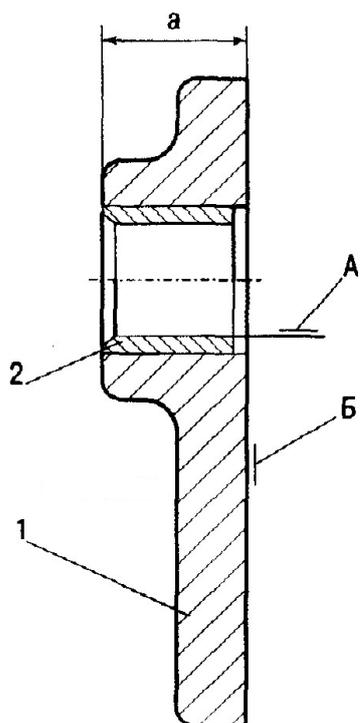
Крышка масляного насоса в сборе со втулкой: 1 - крышка; 2 - втулка; а - размер; А и Б - поверхности
